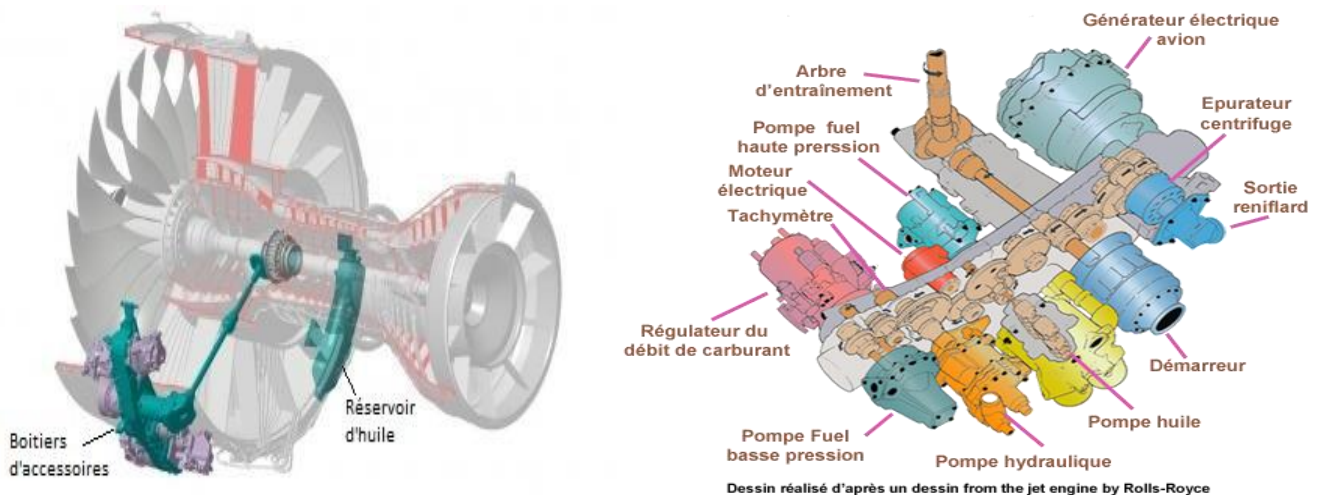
Boîtiers d'accessoires (Accessory Gearbox)
